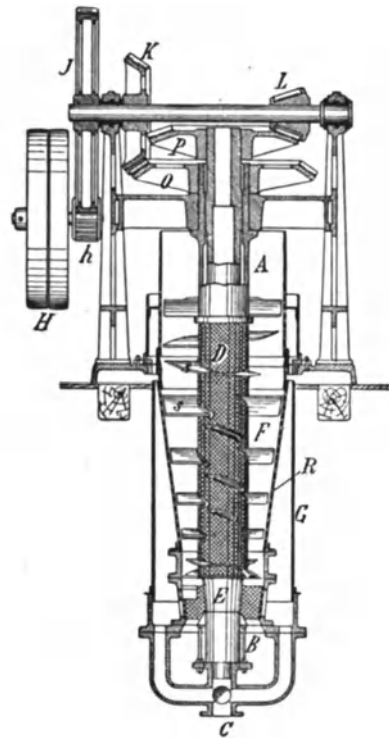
Entwässerungspressen für Rübenschnitzel (Sangerhäuser Maschinenfabrik).
